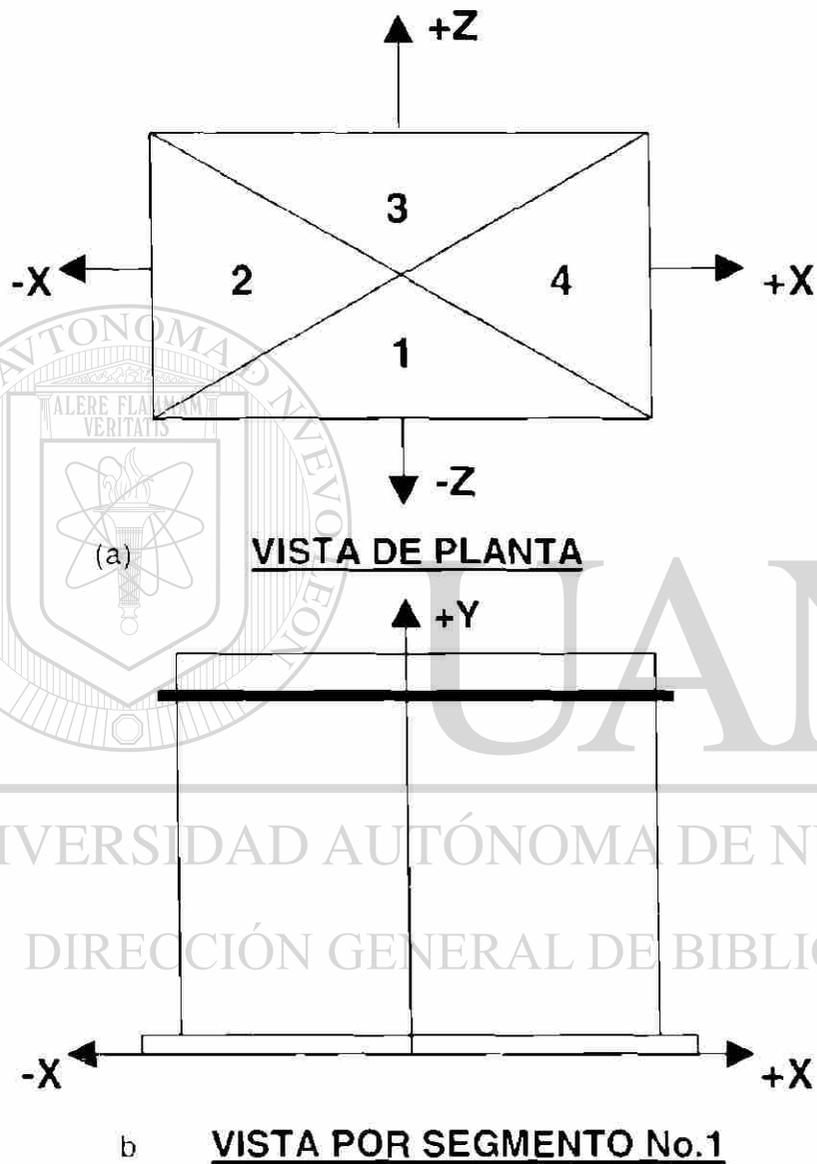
(a) Vista de planta y (b) vista por segmento No.1 para ubicar las coordenadas de los centros de gravedad.
